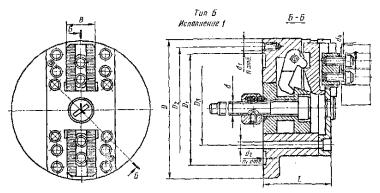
Самоцентрирующий двухкулачковые рычажно-клиновой патрон
